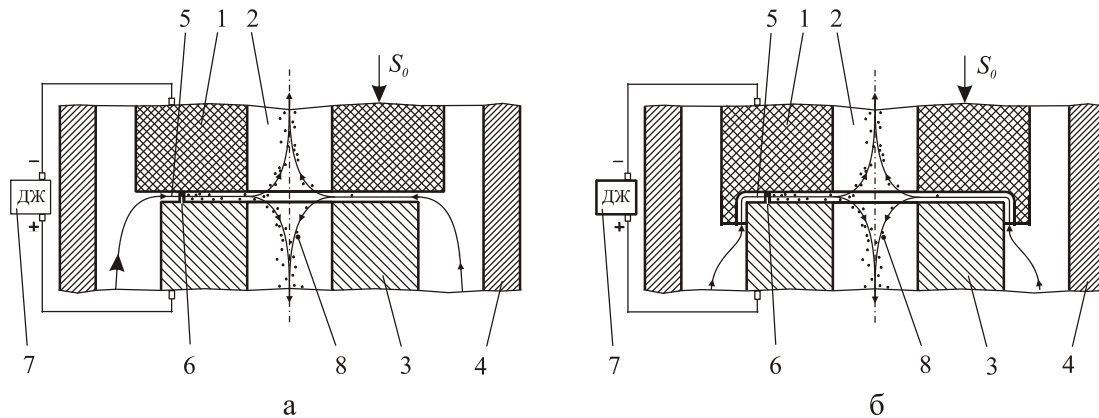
Технологічна схема формоутворення, що використана в роботі [2] для обробки твердосплавного валка: а - початкова фаза; б - кінцева фаза; 1 - графітовий електрод-інструмент; 2 - технологічний отвір; 3 - твердосплавний валок; 4 - герметизована камера; 5 - гідродинамічний потік; 6 - електрична дуга; 7 - джерело живлення постійним технологічним струмом; 8 - продукти ерозії
